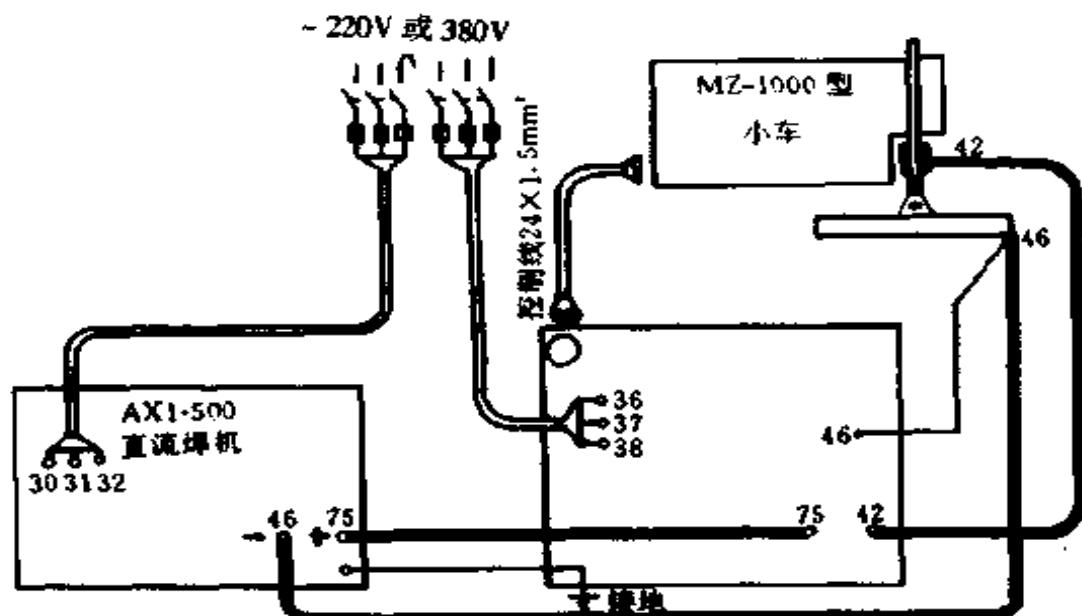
MZ-1000 型焊机外部接线图(直流焊接电源)
